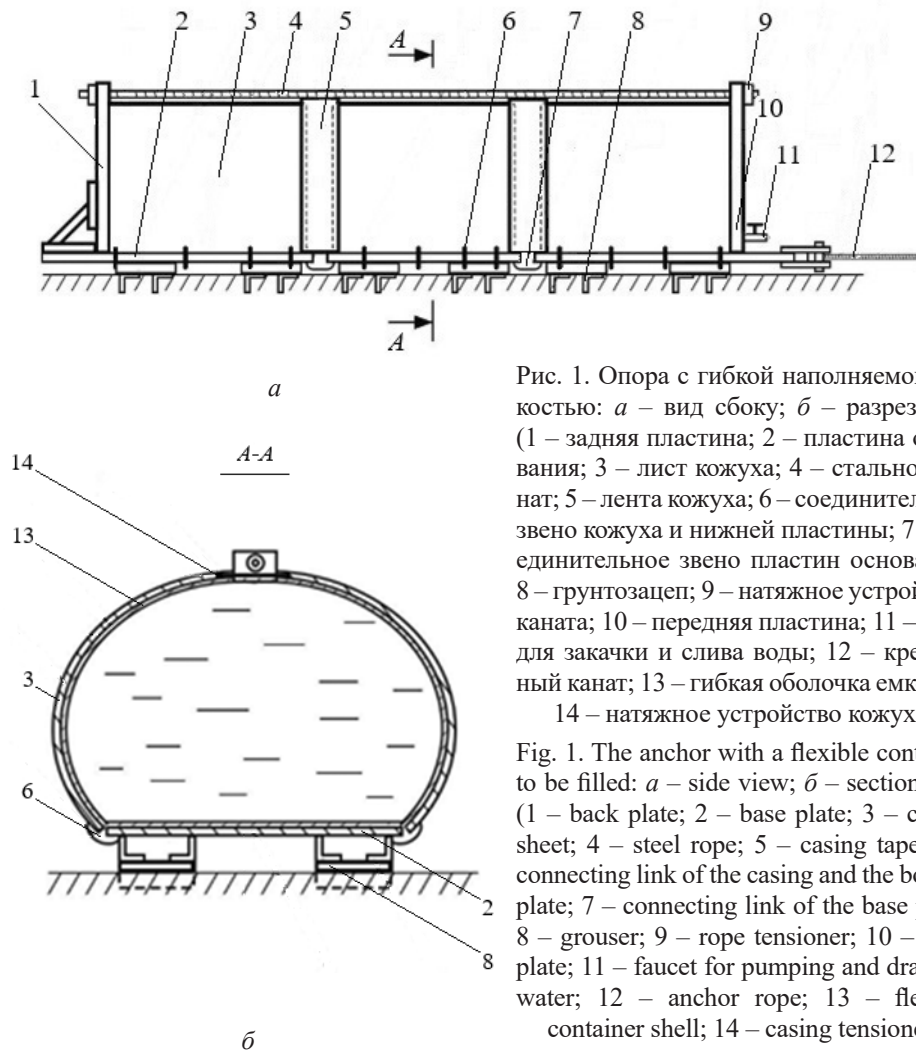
Опора с гибкой наполняемой емкостью: *a* – вид сбоку; *б* – разрез *A-A* (1 – задняя пластина; 2 – пластина основания; 3 – лист кожуха; 4 – стальной канат; 5 – лента кожуха; 6 – соединительное звено кожуха и нижней пластины; 7 – соединительное звено пластин основания; 8 – грунтозацеп; 9 – натяжное устройство каната; 10 – передняя пластина; 11 – кран для закачки и слива воды; 12 – крепежный канат; 13 – гибкая оболочка емкости; 14 – натяжное устройство кожуха)
